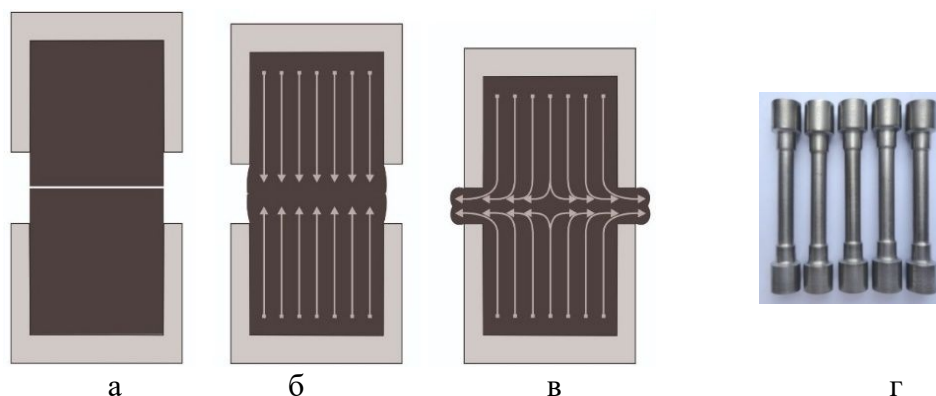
Основные стадии процесса моделирования свариваемых заготовок: форма заготовки после 1-ой (а), 2-ой (б) и 3-ой (в) стадии и образцы, вырезанные из сваренных заготовок (г)
